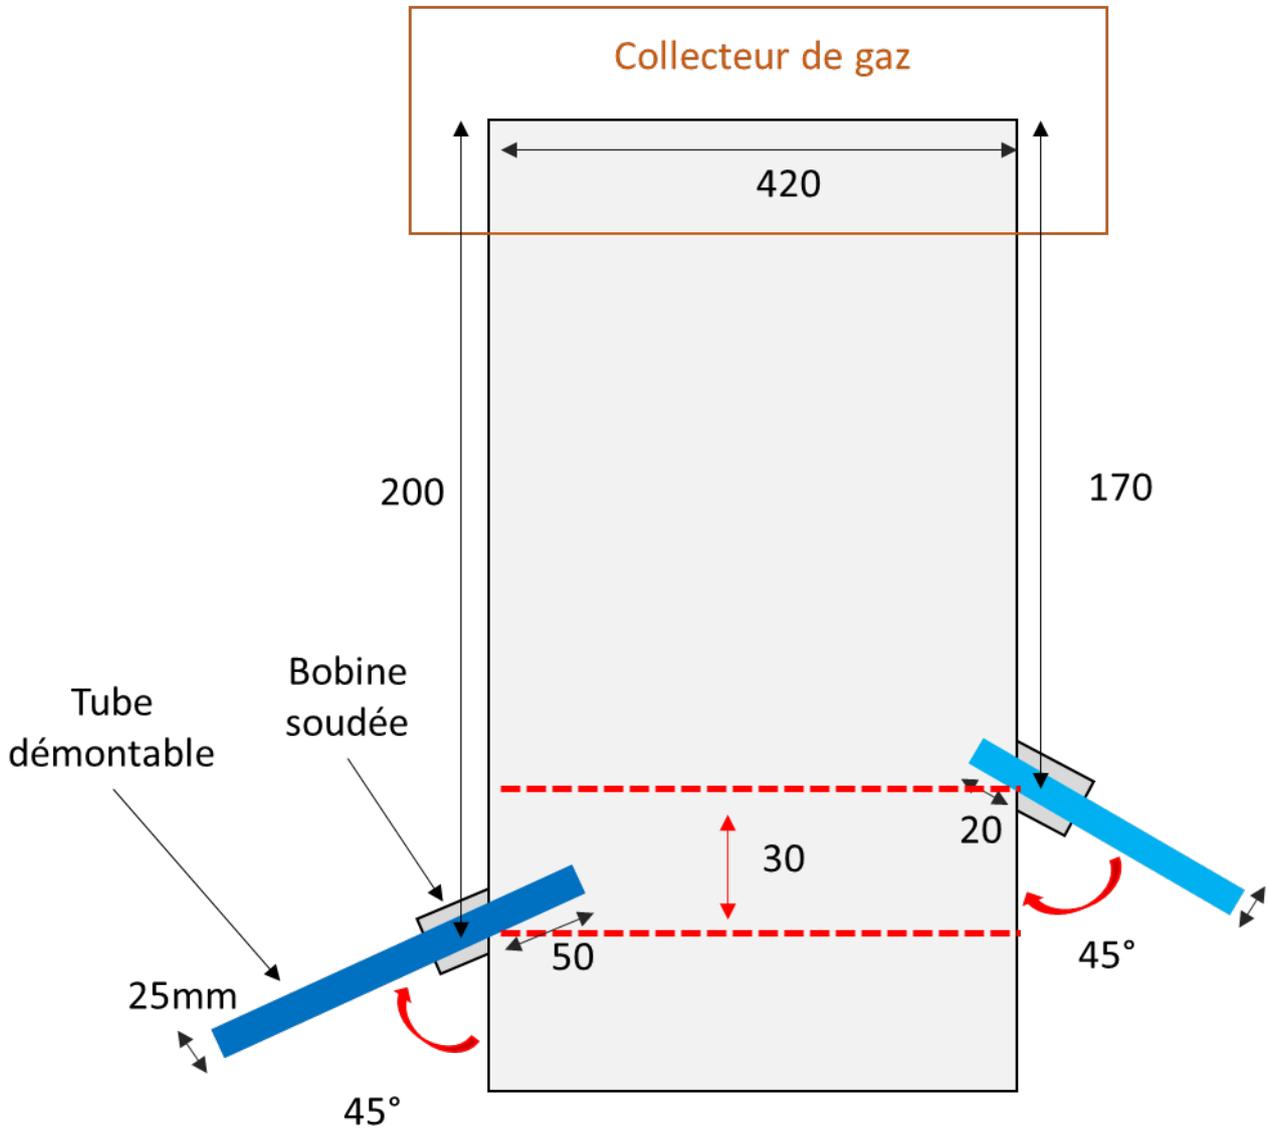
Plan détaillé des injections d'air 2, côtes en mm
